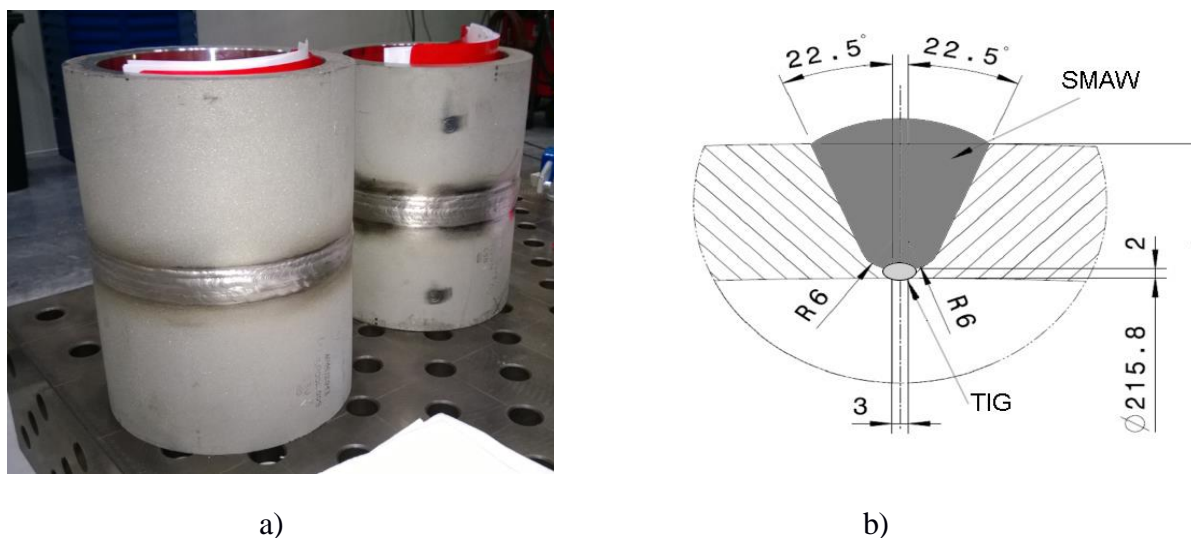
Tubos unidos por solda: a) fotografia das amostras; e b) desenho representativo da solda.
